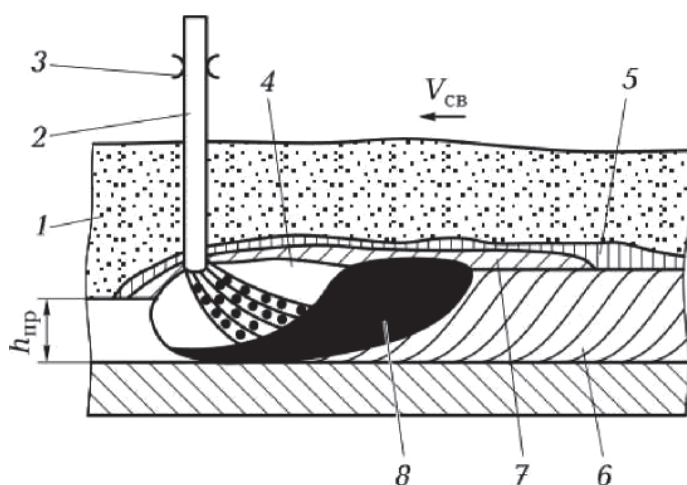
Зварювання під шаром флюсу: 1 – шар флюсу; 2 – електродний дріт; 3 – ковзкий контакт; 4 – газовий міхур; 5 – шлакова кірка; 6 – зварний шов; 7 – розплавлений флюс; 8 – зварювальна ванна
